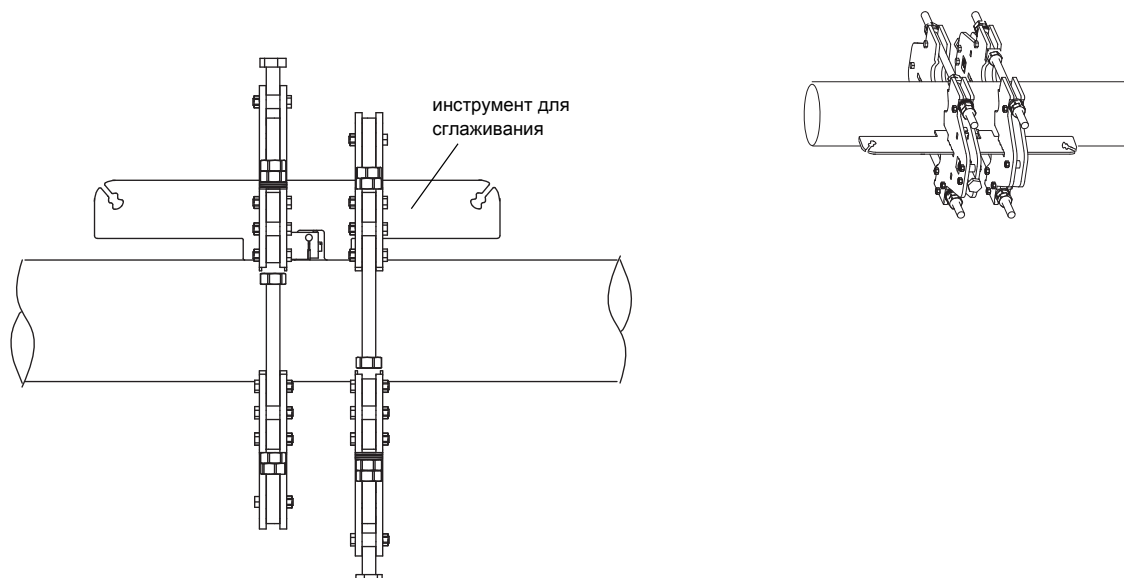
Выравнивание прорезей для стыковочных пластин креплений к трубе
